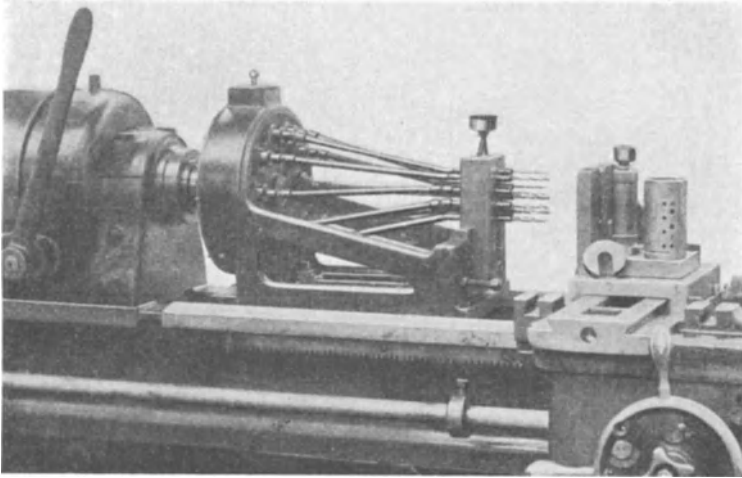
Drehbank als Mehrspindelbohrmaschine umgebaut.
